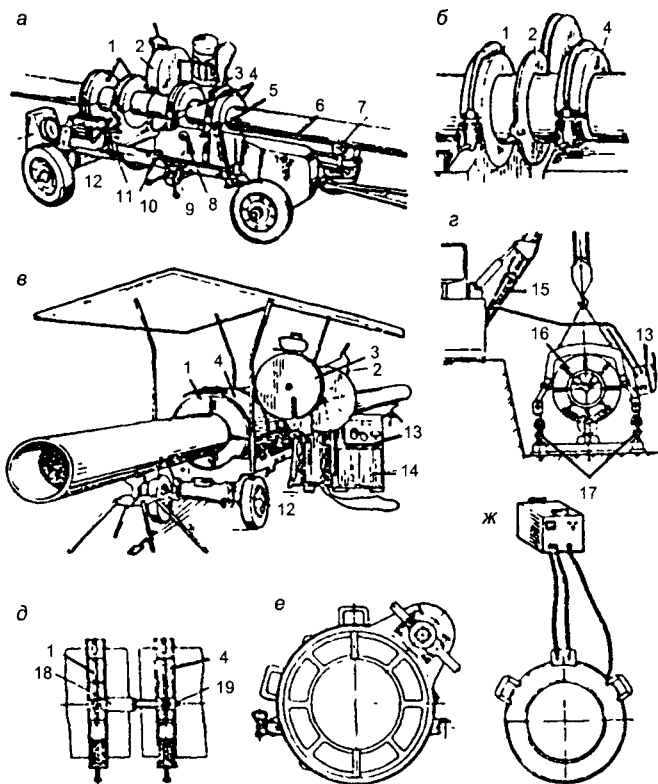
Установки и оборудование для сварки пластмассовых (полиэтиленовых) труб:
